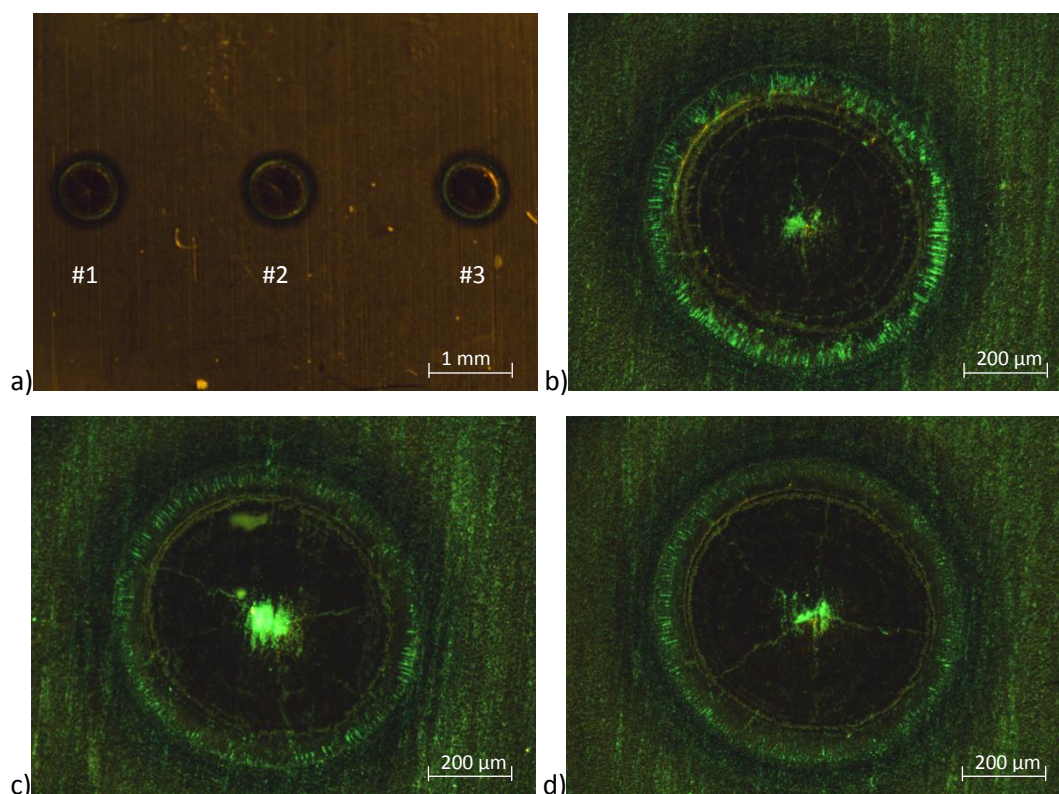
Ensaio soldadura em Ti.
